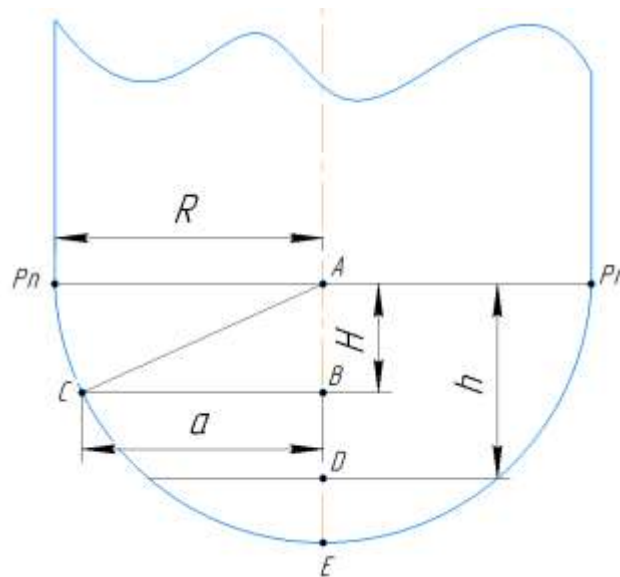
Схема визначення розрахованої висоти вершинки сфероциліндричної фрези при зіткненні з контрольованою поверхнею.
